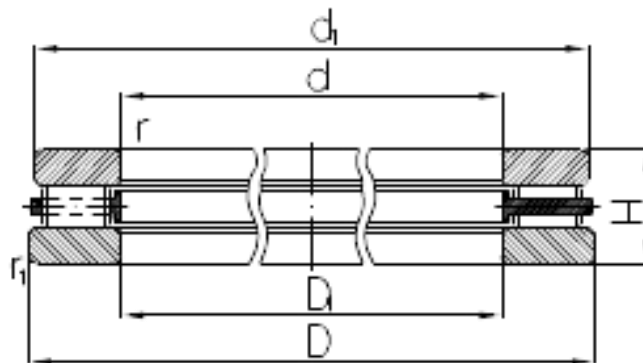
ескіз роликового конічного одинарного підшипника.
